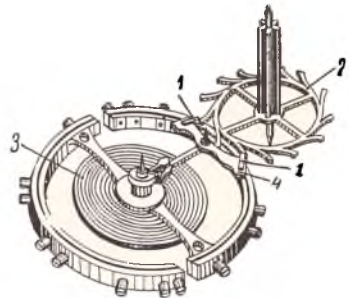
Анкерный палетный ход: 1 — палеты; 2 — анкерное колесо; 3 — баланс; 4 — анкерная вилка
